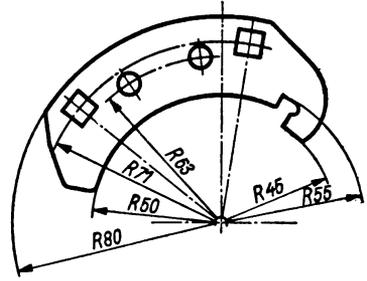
Eintragung mehrerer Halbmesser zu einem Mittelpunkt
